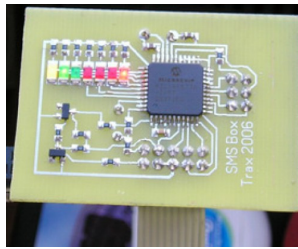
Projeto de Sistema Embarcado soldado em placa de circuito impresso
